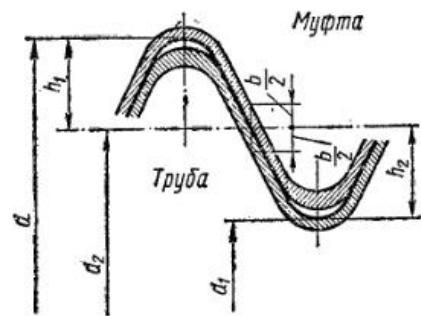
Схема расположения полей допусков трубной цилиндрической резьбы:
